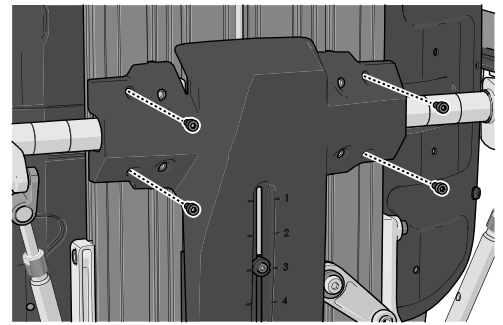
Anbringensorte der vier Schrauben zur Sicherung der Kunststoffabdeckung.
